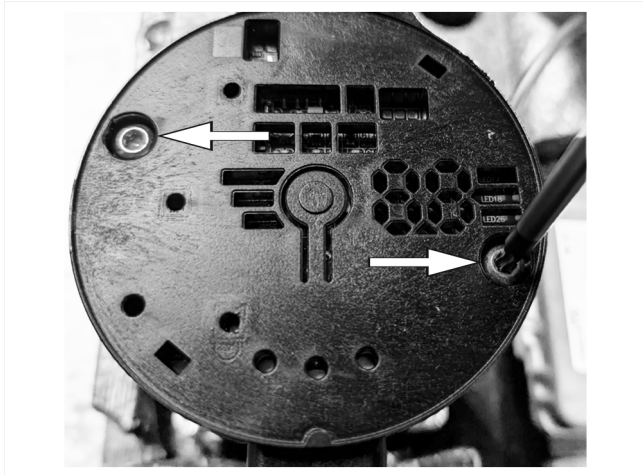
Schrauben der Pumpenelektronik lösen bzw. festschrauben
